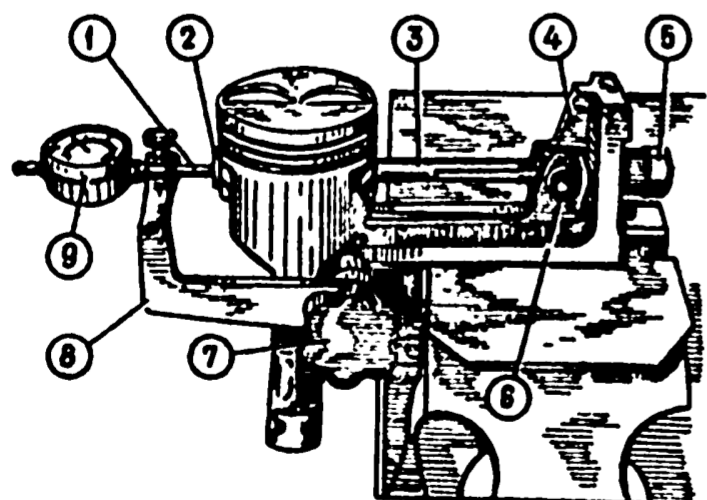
Собранный комплект поршень - палец - шатун, установленный на приспособление А.95615 для испытания на выпрессовку пальца: 1 - штифт индикатора в соприкосновении с концом стержня; 2 - головка стержня в соприкосновении с пальцем; 3 - резьбовой стержень с пазом; 4 - основание; 5 - гайка стержня; 6 - упорный палец стержня; 7 - рукоятка зажима кронштейна; 8 - кронштейн индикатора; 9 - индикатор
